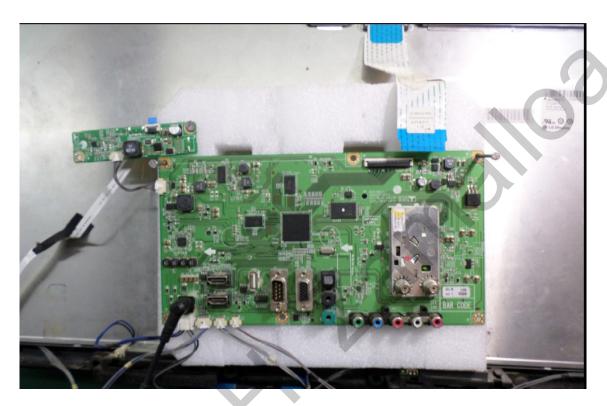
Detalle de las plaquetas sueltas para libre acceso
